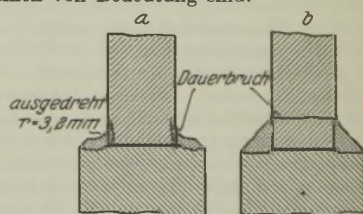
Bruchverlauf in geschweißten Dauerbiegeproben.
